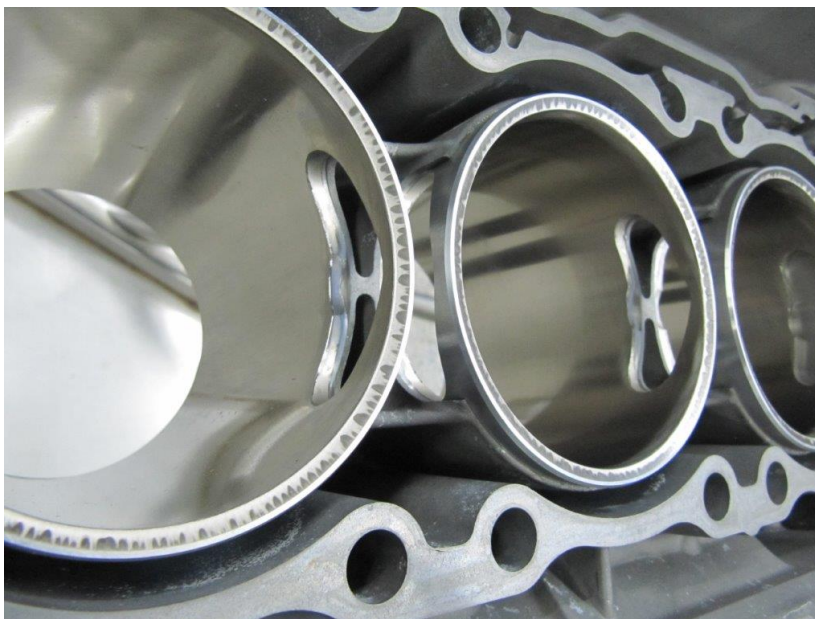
Motor aus Bild 53 mit verlängerten Generation 2 Zylindern, die Kolbenkipper im UT verhindern. Klar erkennbar ist der Überstand über die sichtbare, ehemalige Unterkante der Originalzylinder. Die Aussparungen in den Zylindern zur Montage der Kolbenbolzen sind nun geschlossen und wurden dadurch zu Öffnungen. Ein Vergleich mit Bild 50 bietet sich an.
